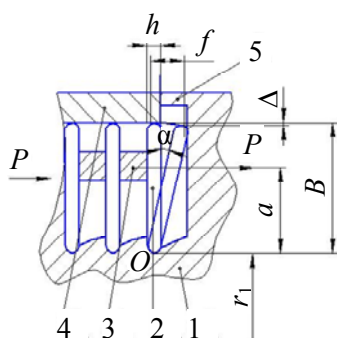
Розрахункова схема сили деформації витків у гвинтовому патроні затиску втулок: 1 — корпус оправки; 2 — гвинтовий затискний елемент; 3 — розпорний гвинтовий елемент; 4 — трубчаста заготовка; 5 — упор
